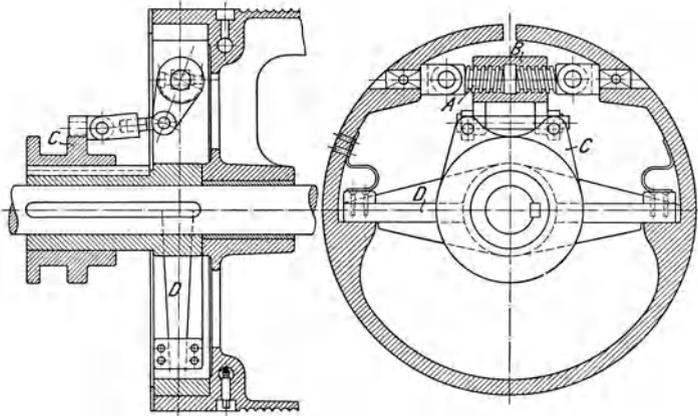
und 391. Spreizringkupplung mit Schraube.
